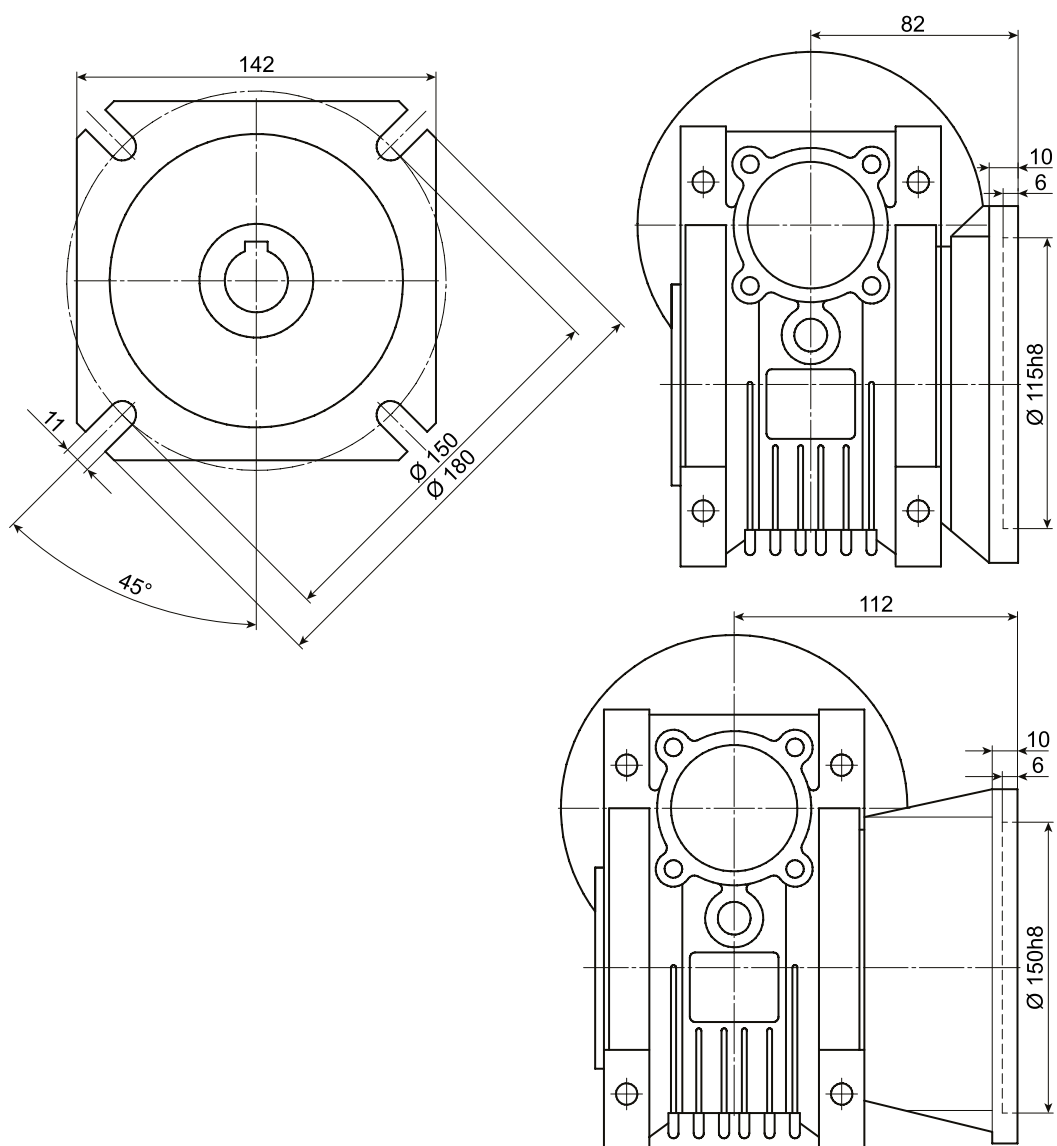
Габаритные размеры боковых фланцев FA и FB
